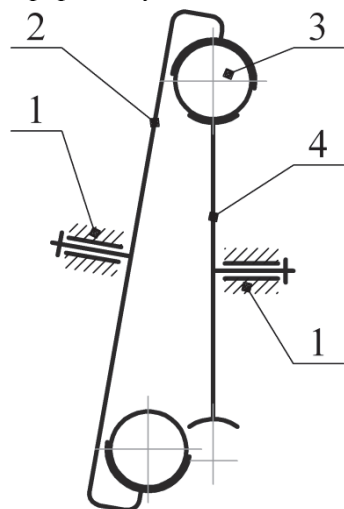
Кинематическая схема шариковой передачи: 1) стойка; 2) обойма; 3) тело качения; 4) колесо
